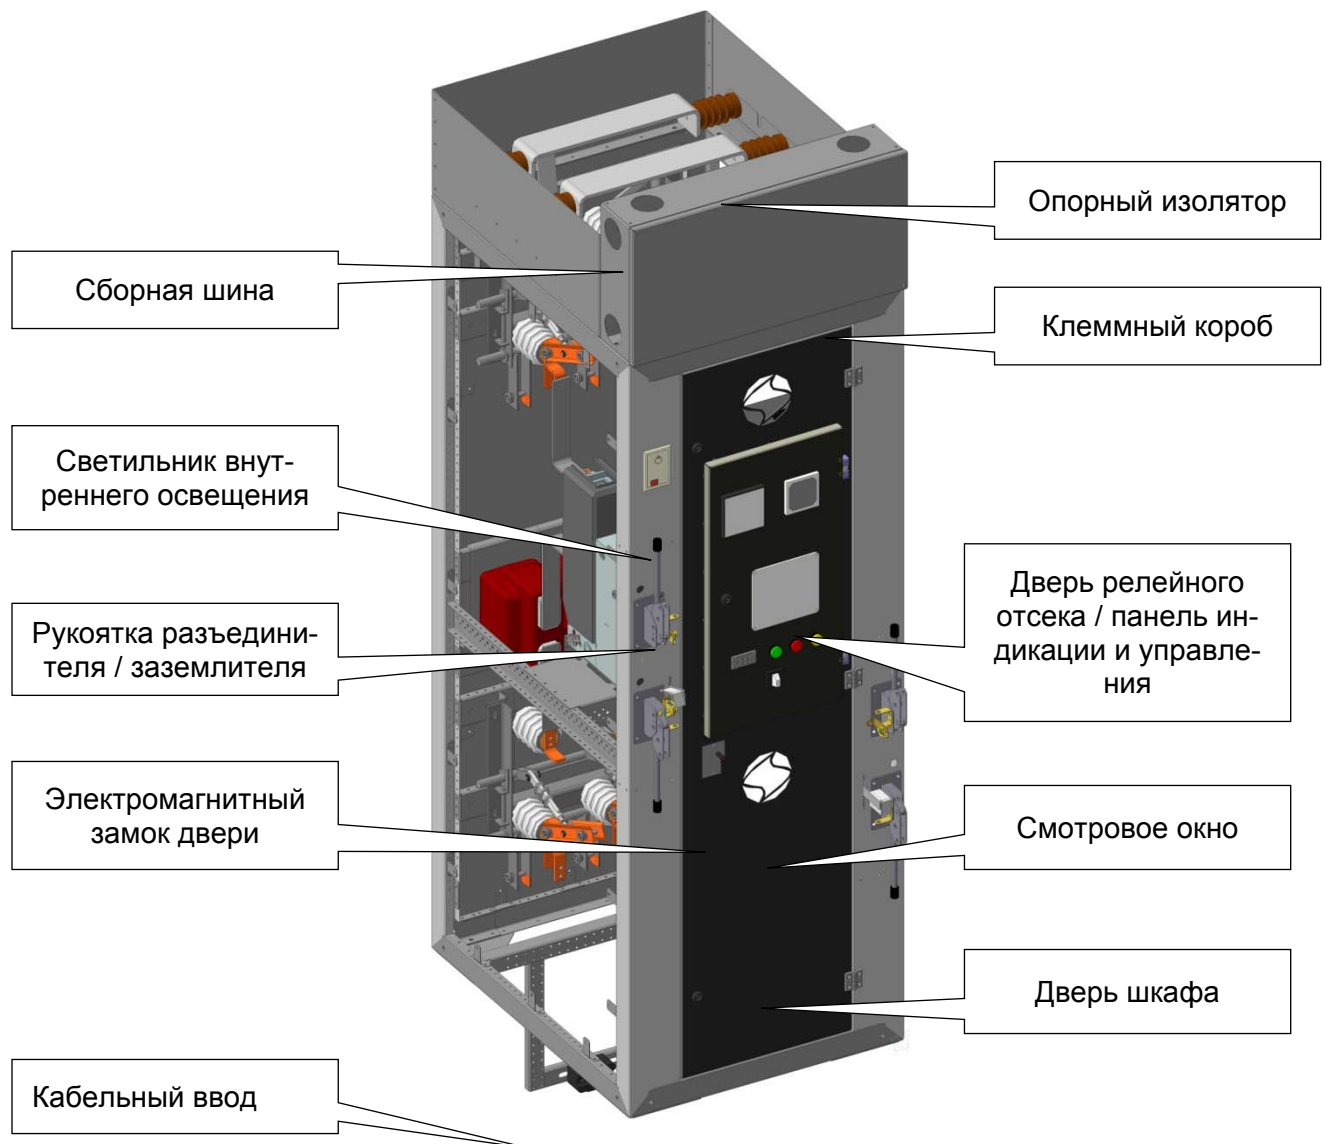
Внешний вид ячейки типа КСО-212, шкаф шинного соединителя в рабочем состоянии.
